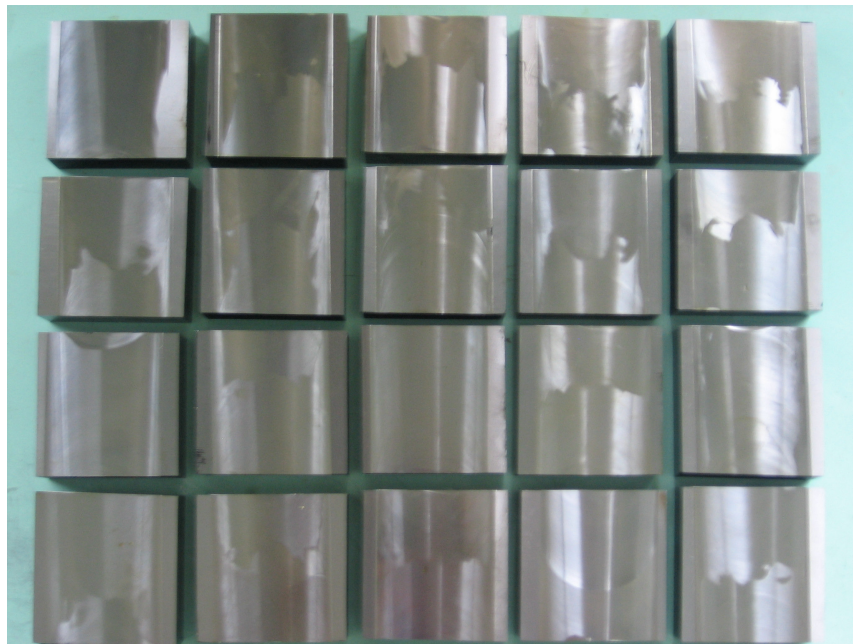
Corpos de prova utilizados para os ensaios de usinagem
